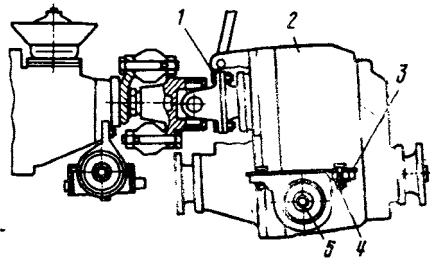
Схема установки раздаточной коробки автомобиля ВАЗ-2121:
